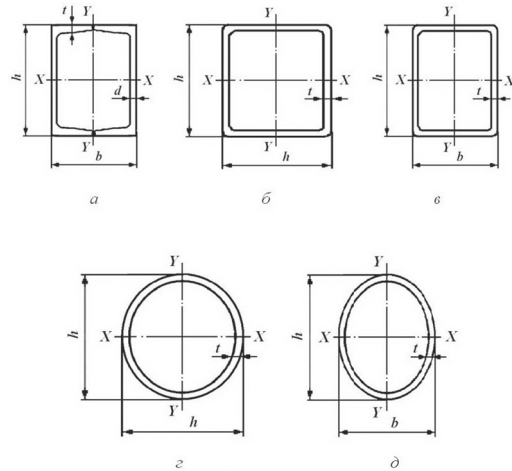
Формы полых поперечных сечений рычага: а – коробчатое из двух швеллеров; б – квадратное; в – прямоугольное; г – круглое; д – овальное; h – высота сечения, м; b – ширина сечения, м; d, t – толщина стенки сечения, м
